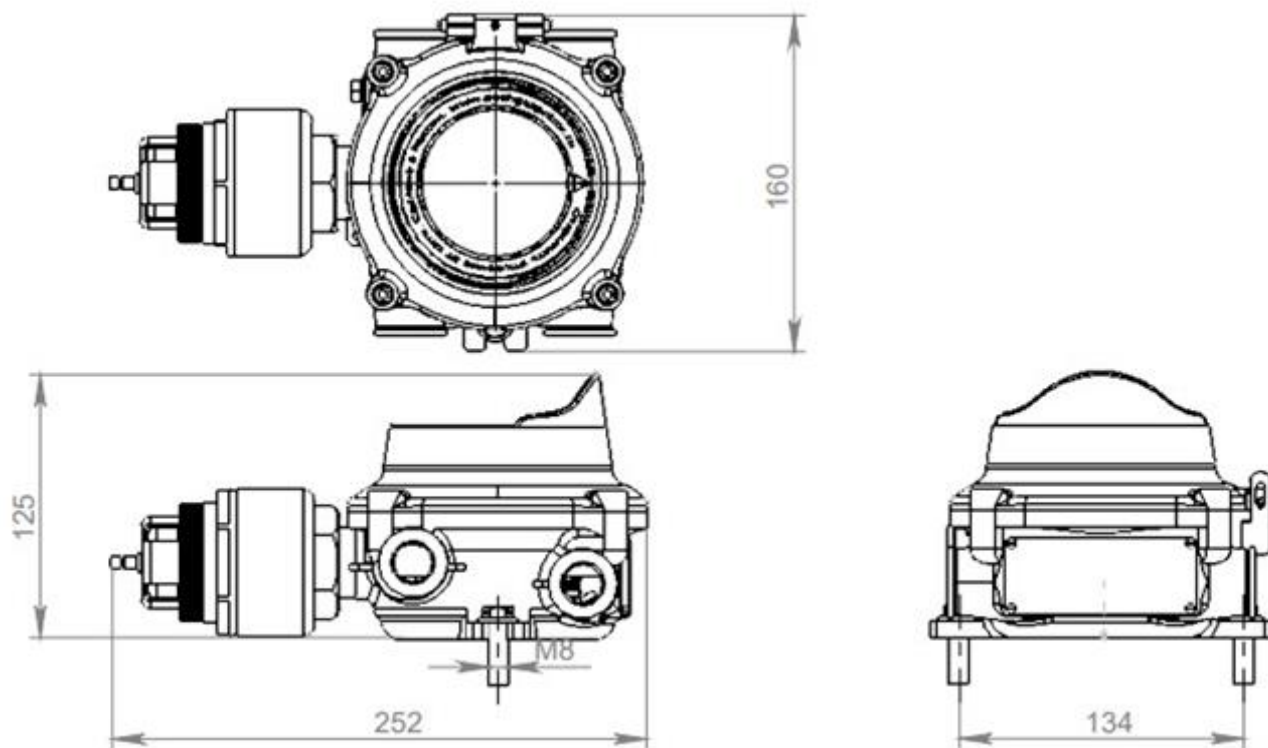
Габаритный чертёж изделия с 5-ю вводными отверстиями
